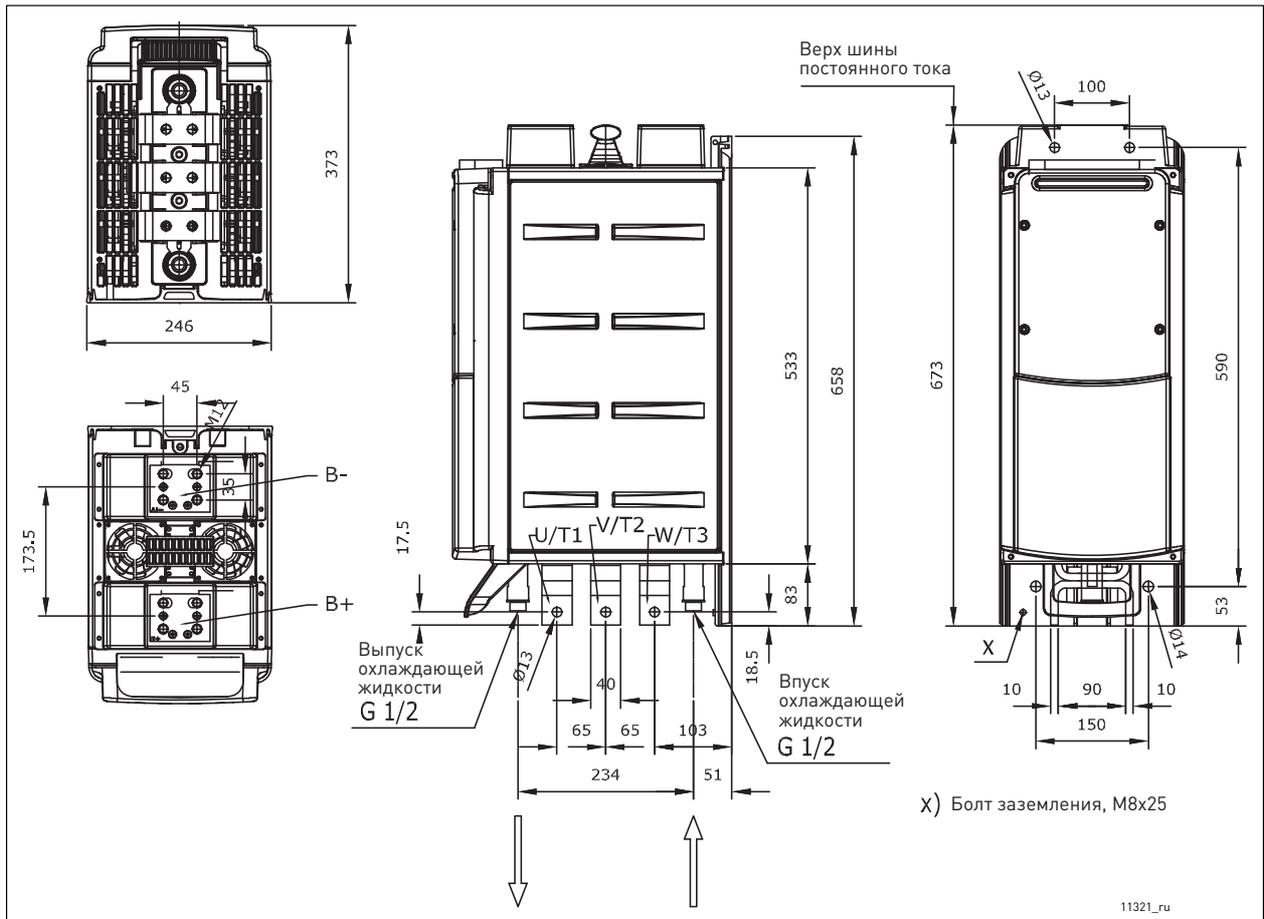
Инвертор VACON® Liquid-Cooled, CH62
